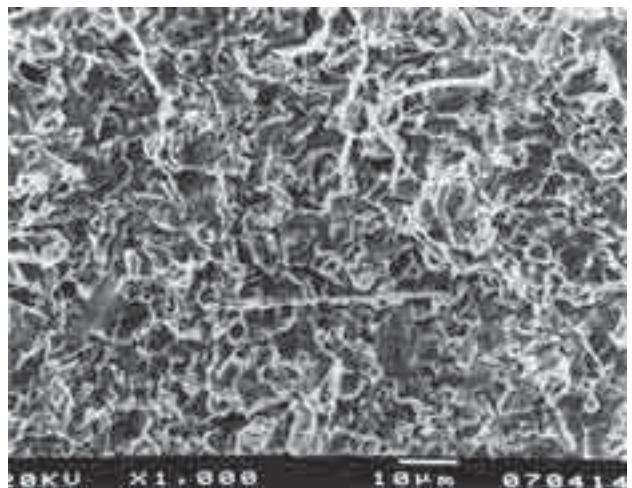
MEV da fratura frágil no corpo-de-prova na condição soldado por brasagem; 1000X.
